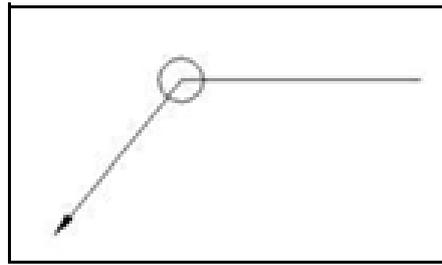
Indicación de soldadura continua alrededor de la unión.
